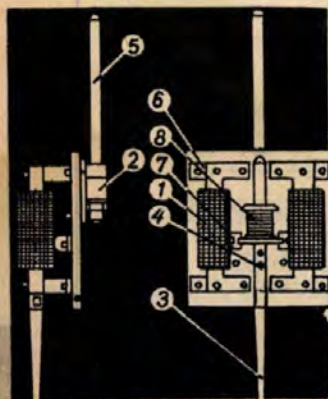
Capul de lucru al mașinii ultrasonore de tăiat și găurit: 1 — bobină de premagnetizare; 2 — bucle; 3 — concentrator-sculă; 4 — vibrator magnetostriktiv; 5 — tijă de fixare a capului; 6 — tole; 7 — bară; 8 — bobină de excitație
